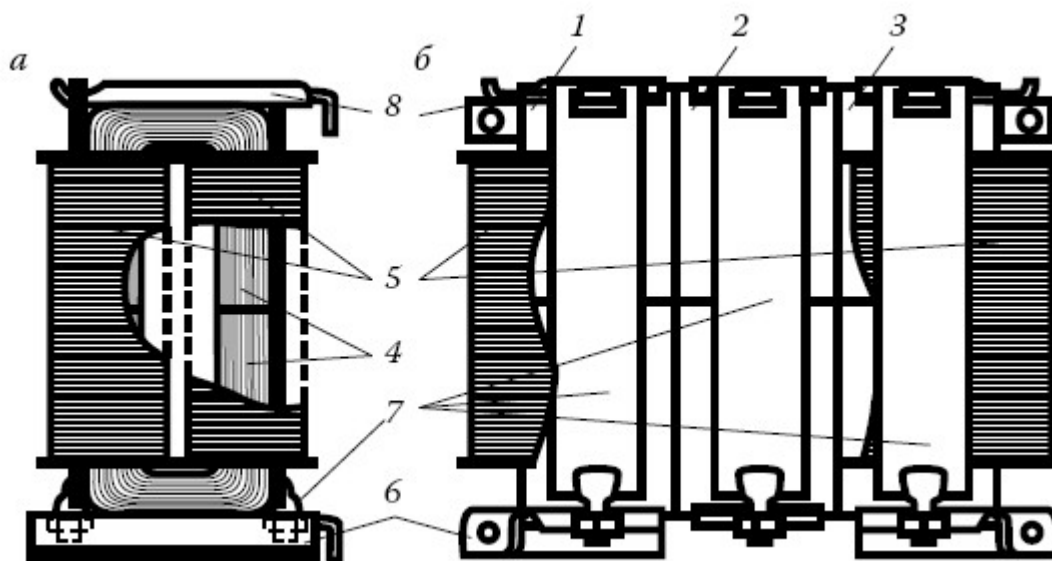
Сварочный трансформатор из телевизионных трансформаторов:
